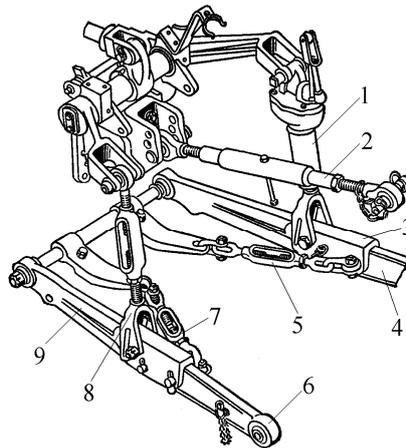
Начіпний механізм трактора ЮМЗ-80/82:
